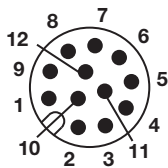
Piedinatura connettore S284 (M12, 12 poli, vista in pianta sul connettore sulla testa sensore)
